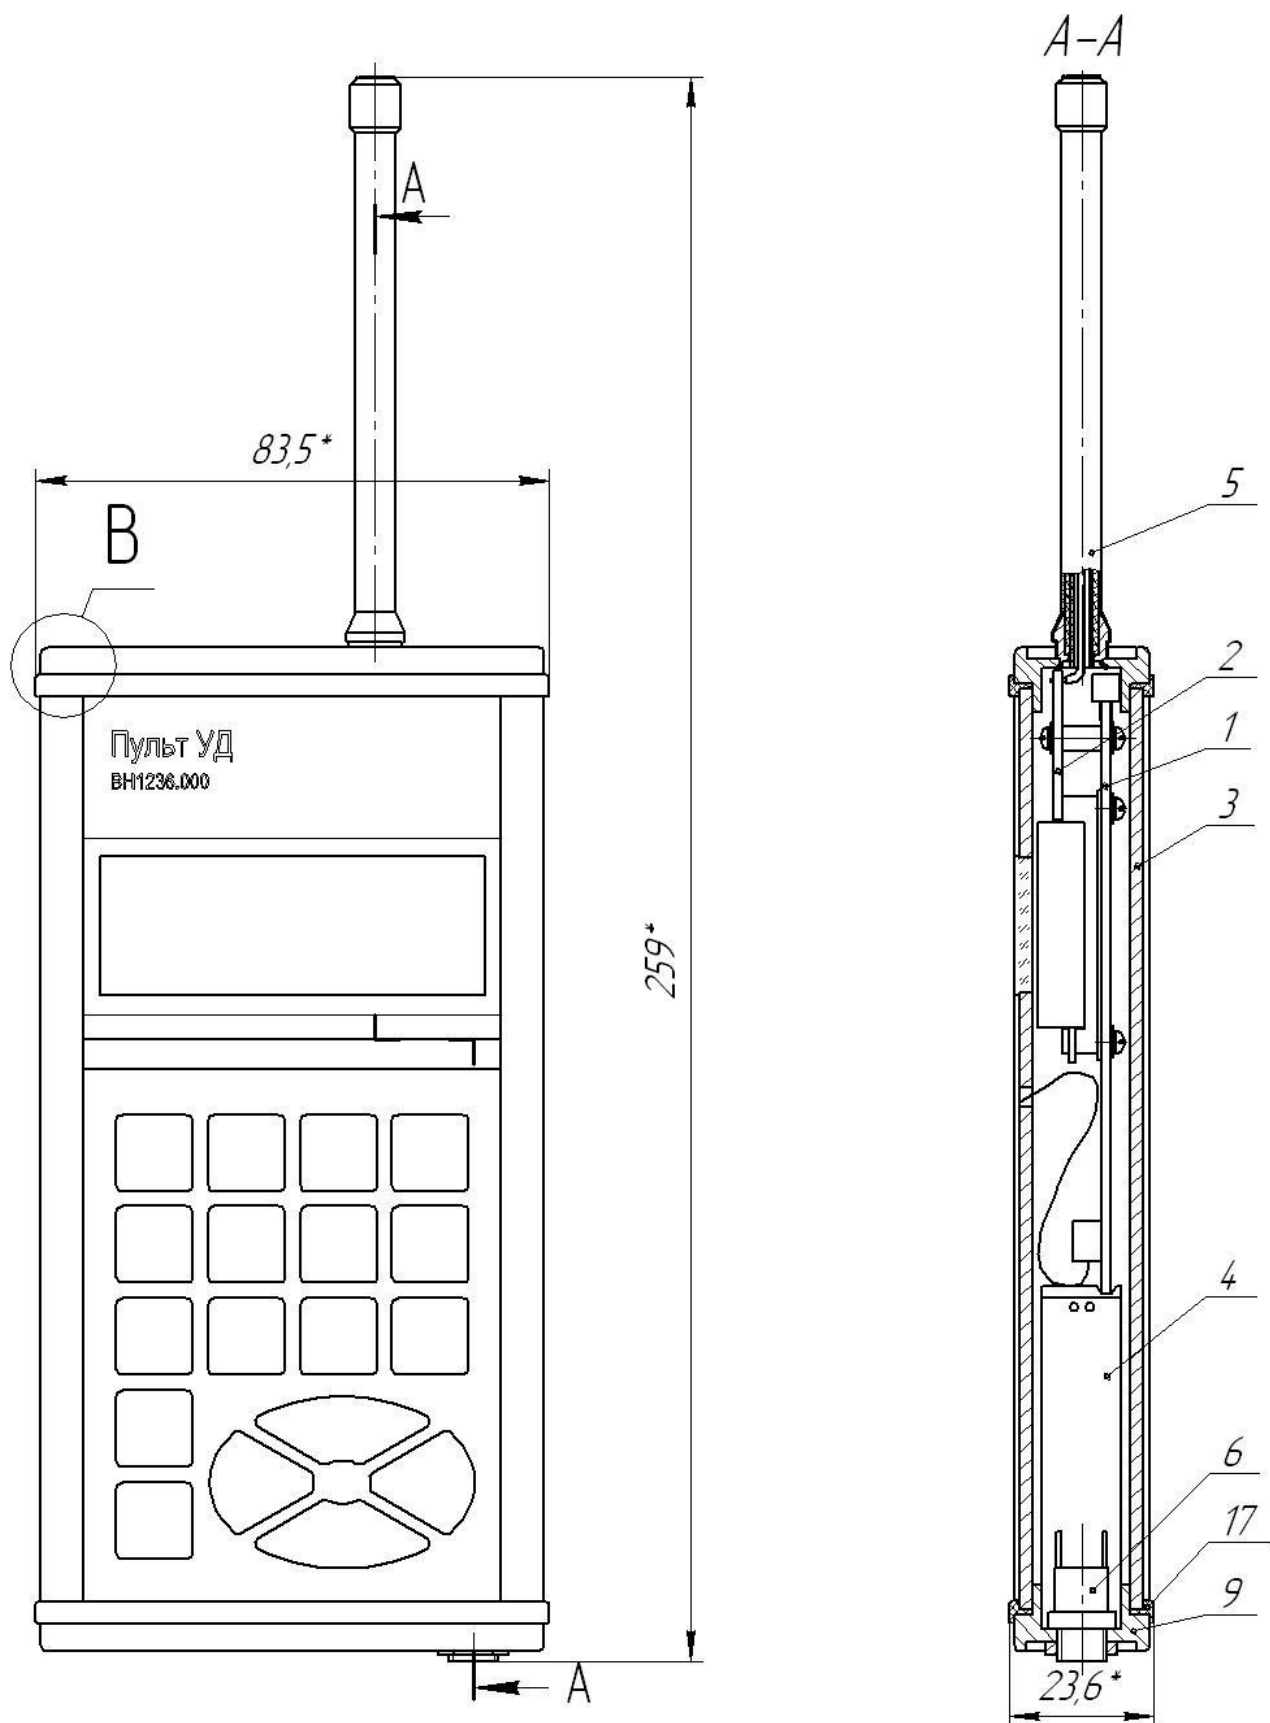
Внешний вид, конструкция, габаритные размеры ПУД.
